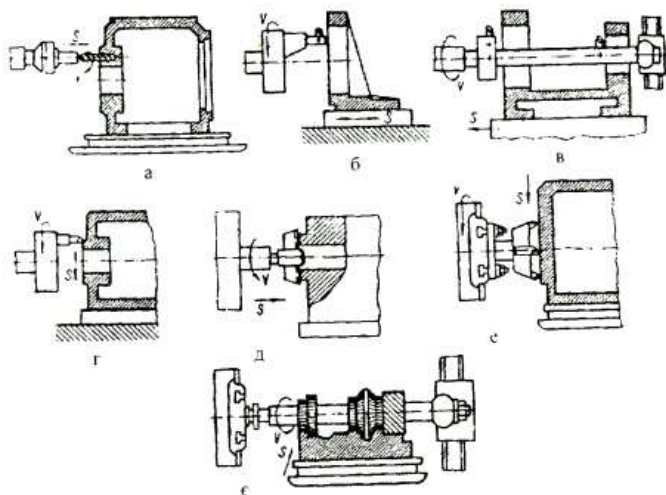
Схеми обробки заготовок на горизонтально-розточувальному верстаті
